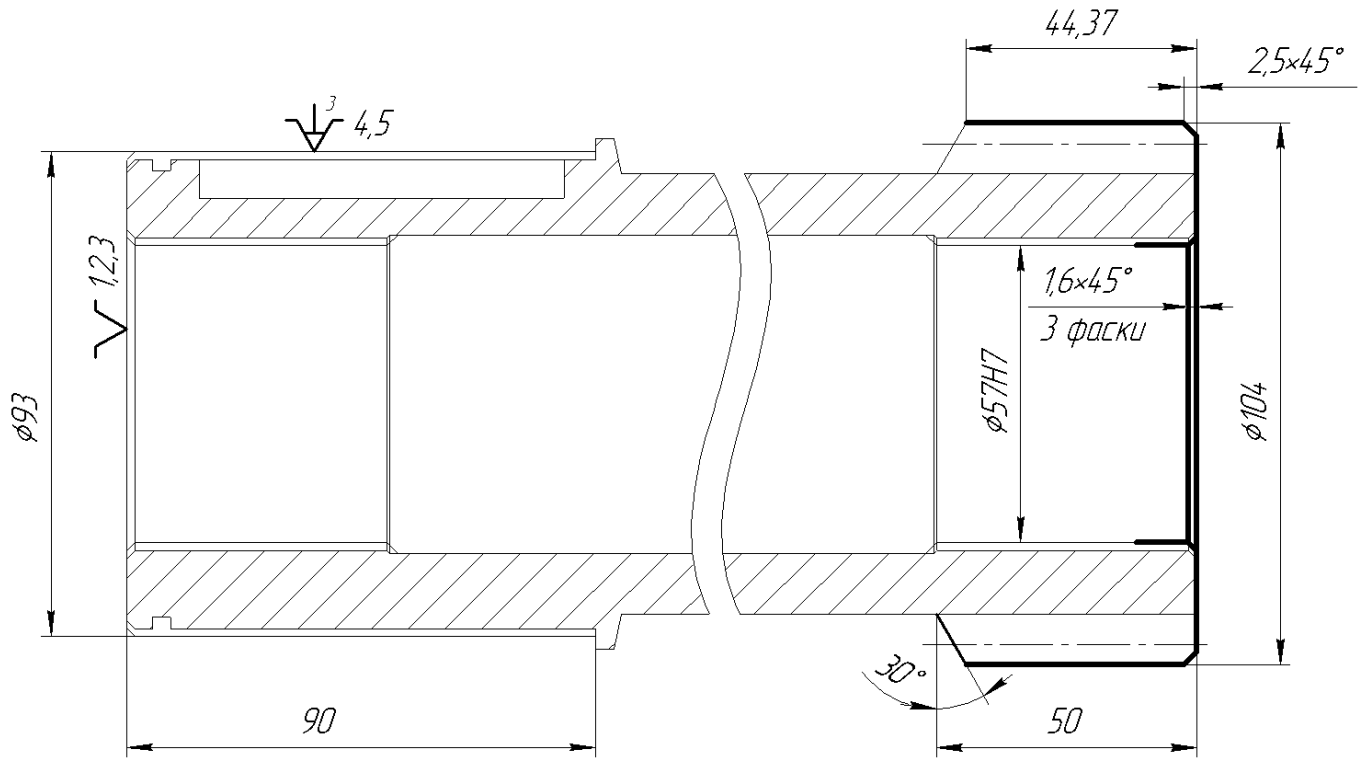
Схема базування і закріплення на операції 015 «Токарно-фрезерна з ЧПК» – установ 2
